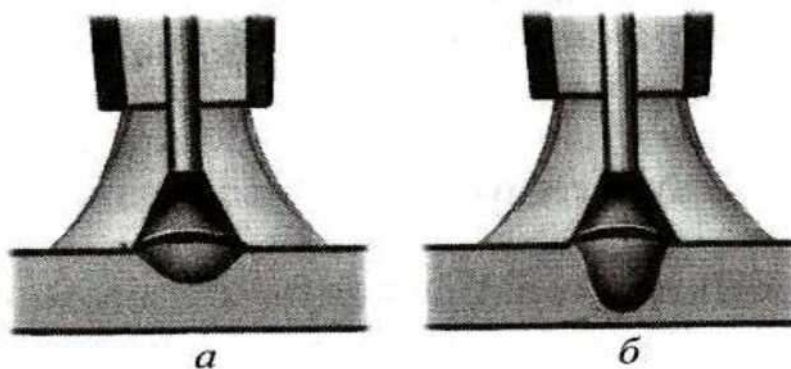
Влияние сварочного тока 100 А (а) и 200А (б) на глубину проплавления
